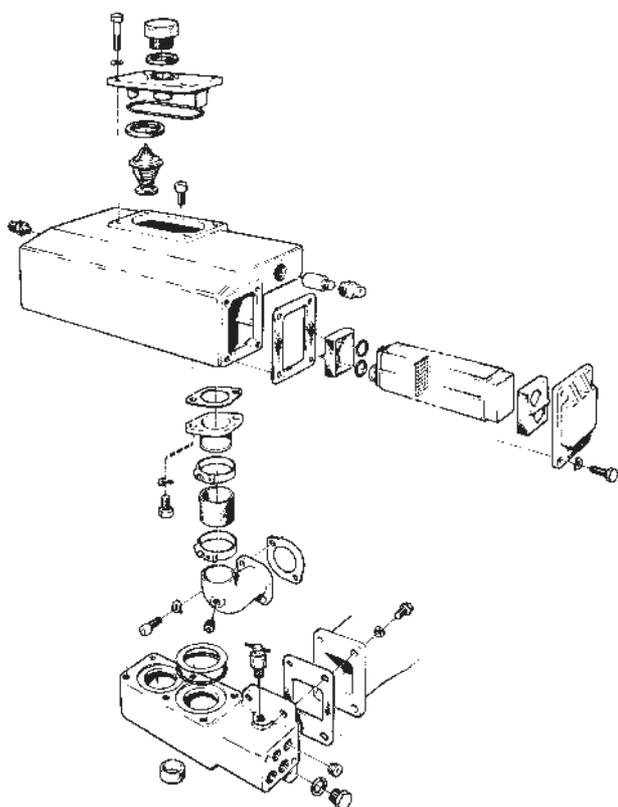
Echangeur thermique, boîtier de thermostat TAMD60
